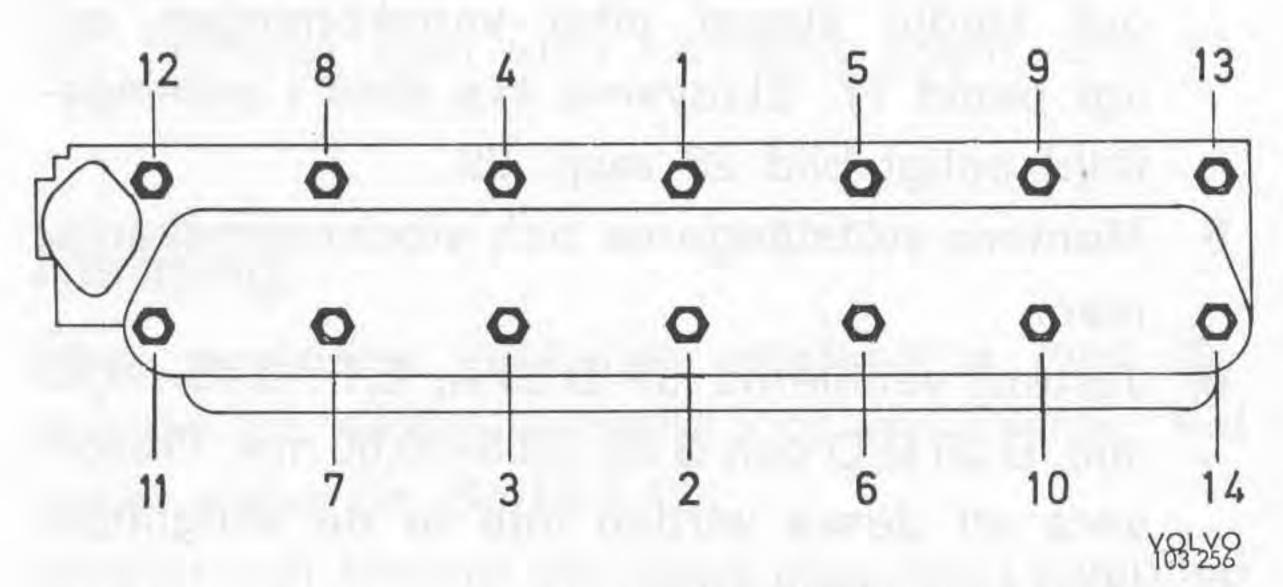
Åtdragningsföljd för cylinderlocksskruvar,
